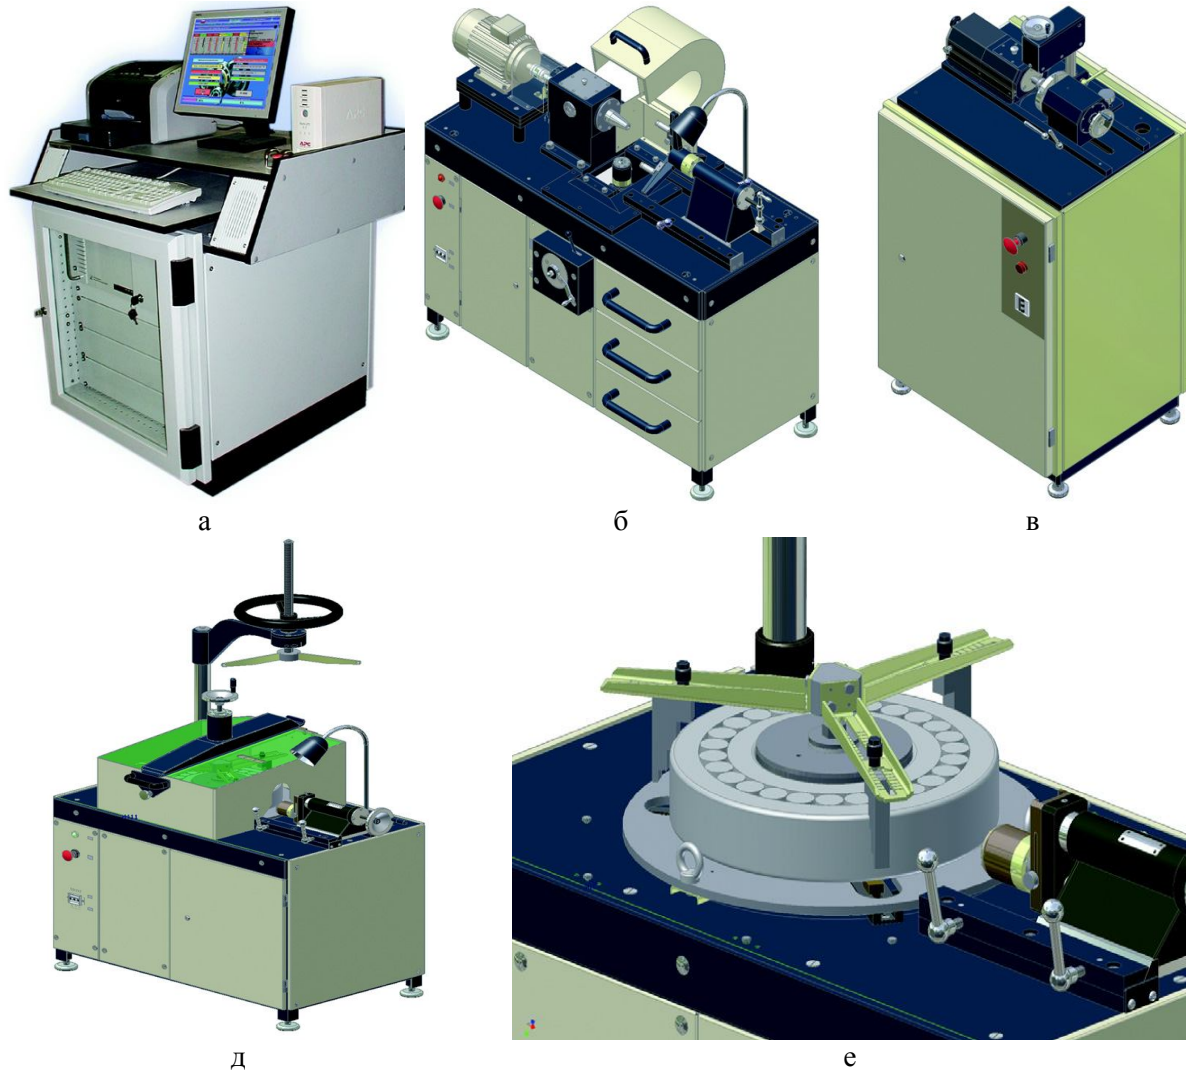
Загальний вид і склад системи КОМПАКС®-РПП: а – діагностична станція; б – привод 1602; в – привод 1608; д – привод 1607; е – привод 1607 з підшипником, без кожуха
